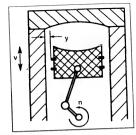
Поперечное сечение цилиндра двигателя и поршня для оценки параметров течения смазочного масла
